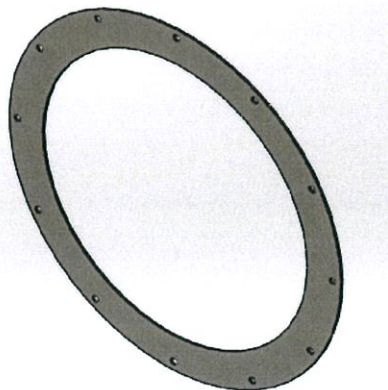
Dimension ของ Feeder pipe (ด้านหน้า)
